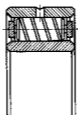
Радиальный роликовый подшипник с витыми роликами
